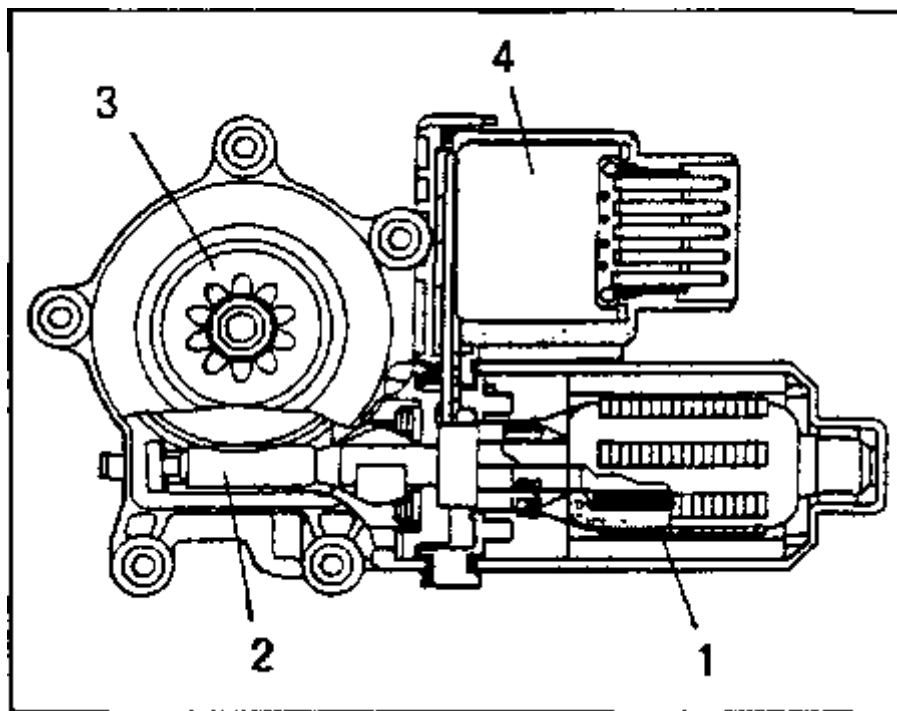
Моторредуктор скла підйомника. (1 - електродвигун; 2 - черв'ячний редуктор;
